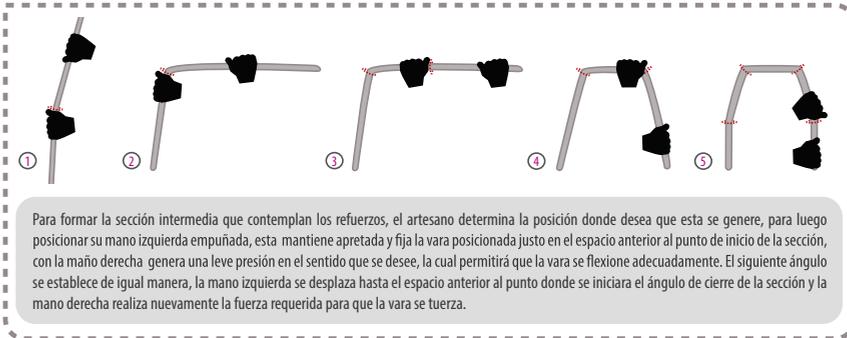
Imagen X Proceso constructivo de refuerzos inferiores, Elaboración propia.
